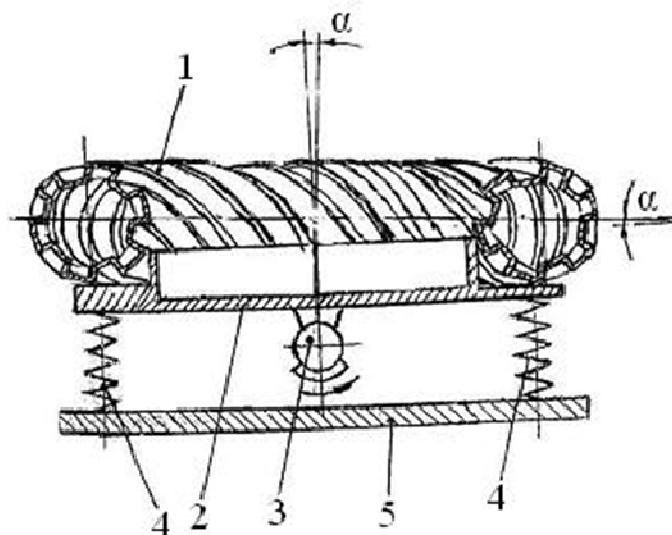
Вибрационное устройство для приготовления кормов
